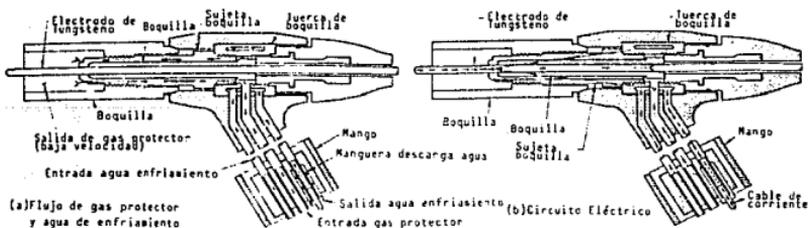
Vistas seccionales de un soplete típico enfriado por agua para soldadura manual por arco con Tungsteno y gas.
